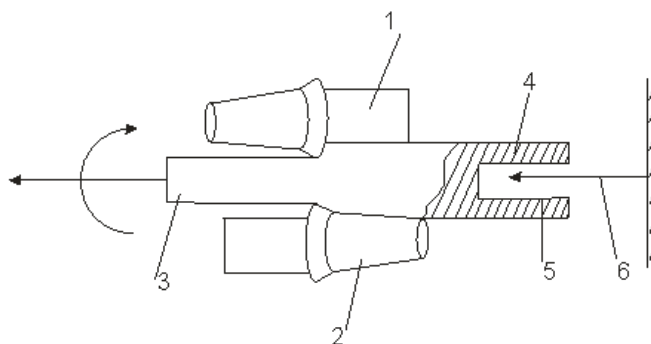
Поперечно-винтовая прокатка: 1,2 – правый и левый валок; 3 – заготовка; 4 – гильза; 5 – оправка; 6 – штанга
